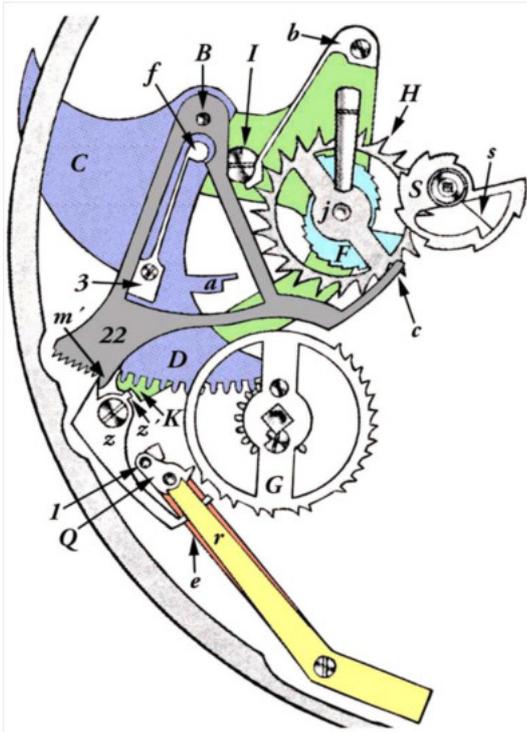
Cadrature à quarts à un seul marteau, de Lépine.
